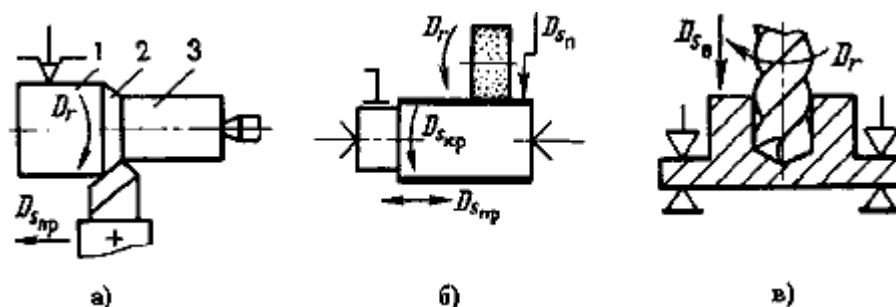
Схемы обработки заготовок: а – точением; б – шлифованием на круглошлифовальном станке; в – сверлением
